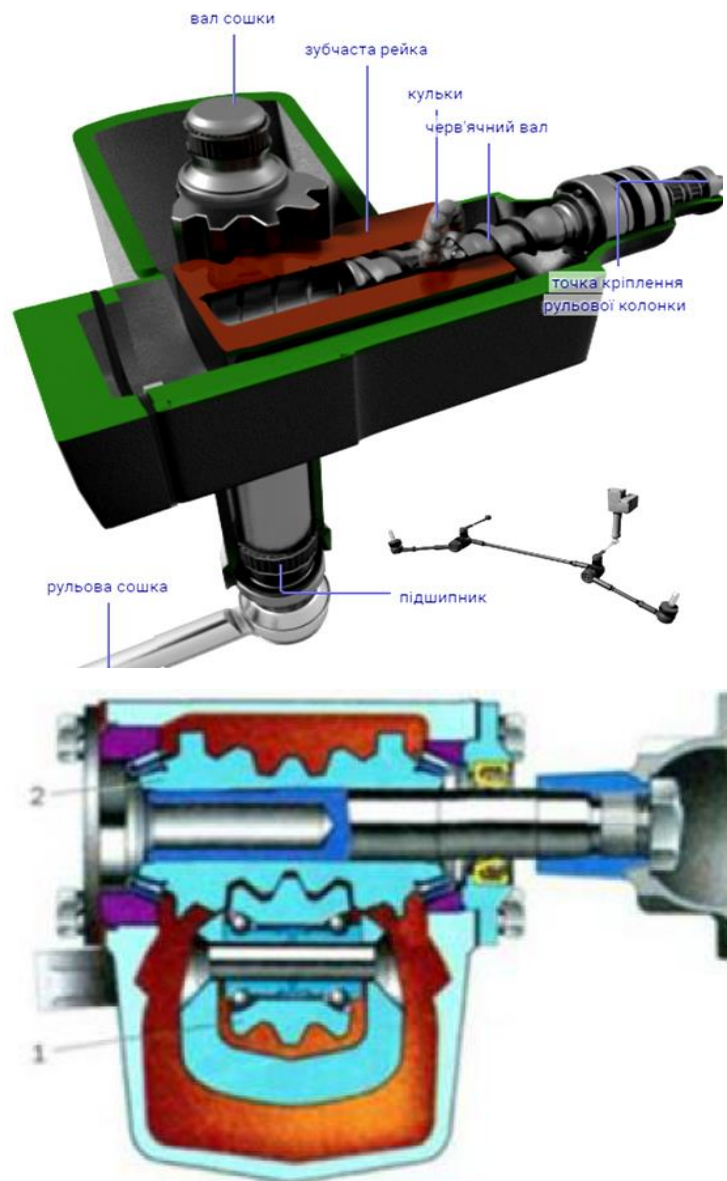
Черв'ячний рульовий механізм: 1 – ролик; 2 – черв'як
